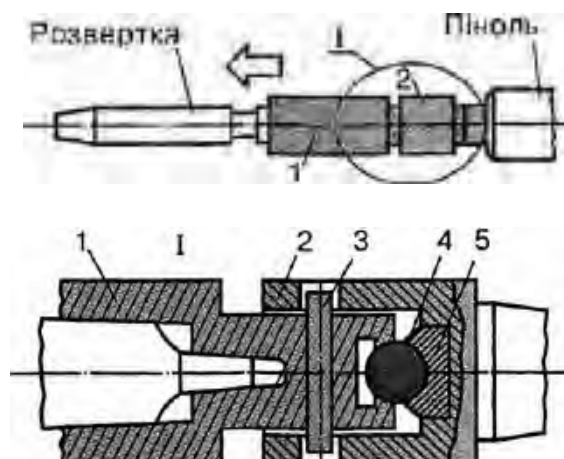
ХИТНА ОПРАВКА ДЛЯ РОЗВЕРТКИ
